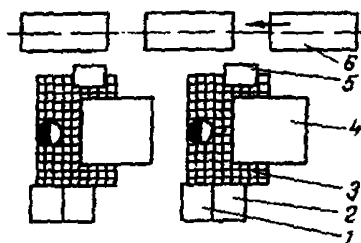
Схема планировки рабочего места формовщиков при безраздельной безопочной формовке:
